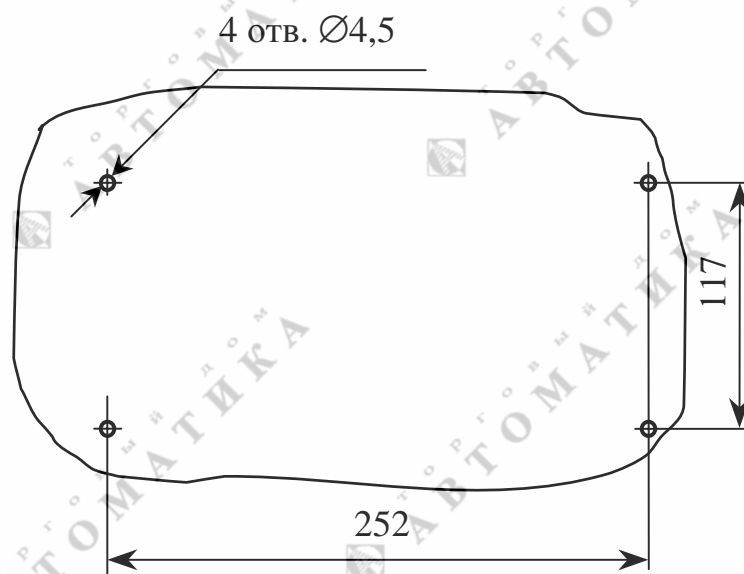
Разметка отверстий для крепления блока преобразовательного настенного исполнения
